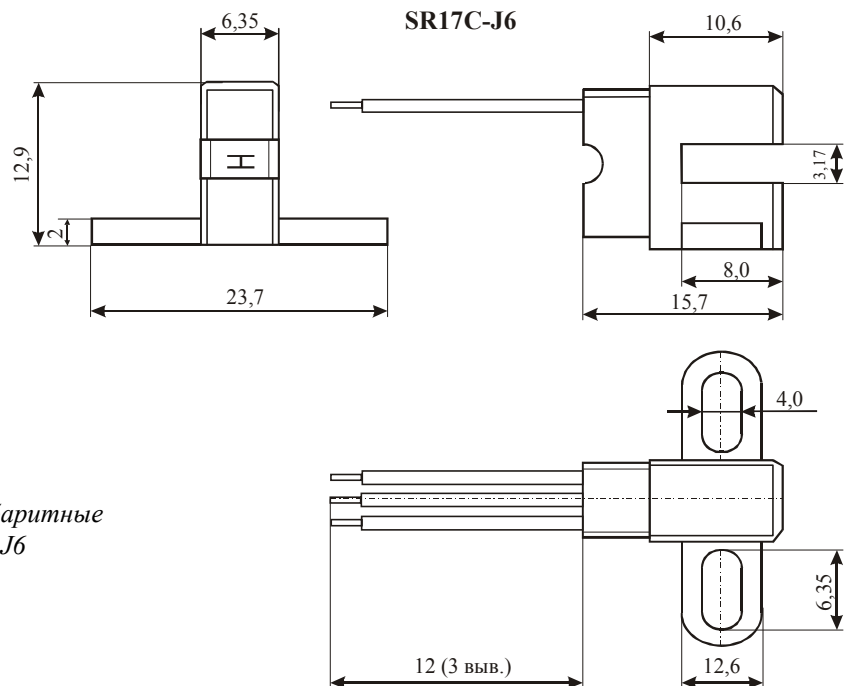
Внешний вид и габаритные размеры ЦМД типа SR17C-J6
